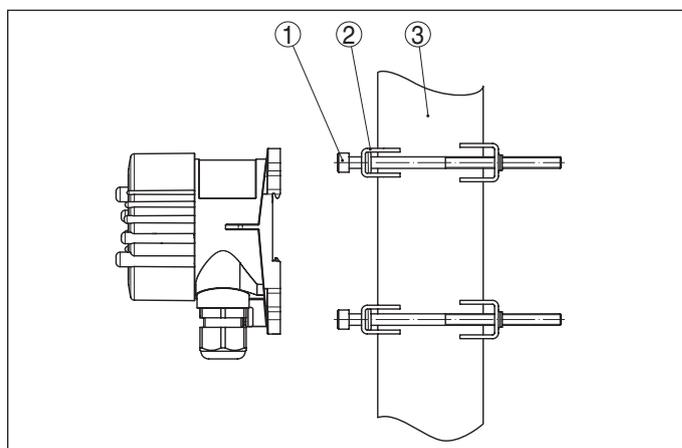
VEGADIS 81, 82 per il montaggio su tubo
